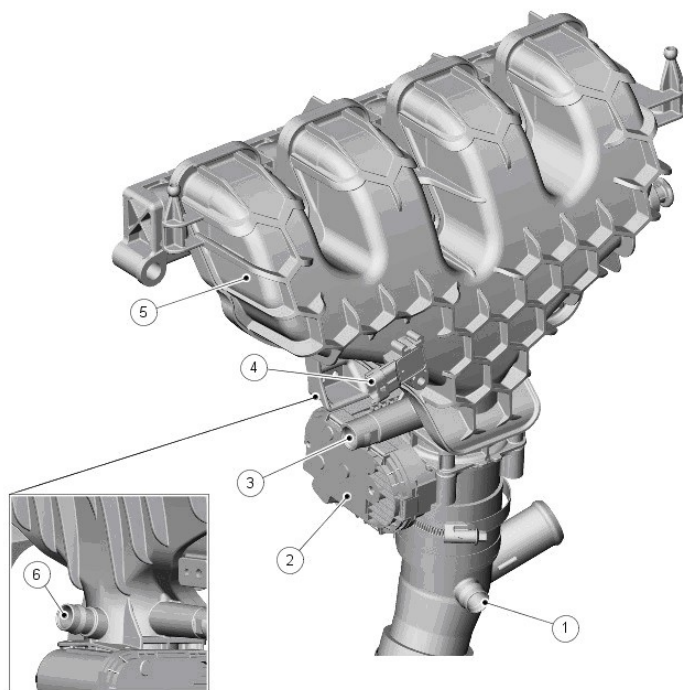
Впускной коллектор бензинового двигателя 2.0L GTDi
